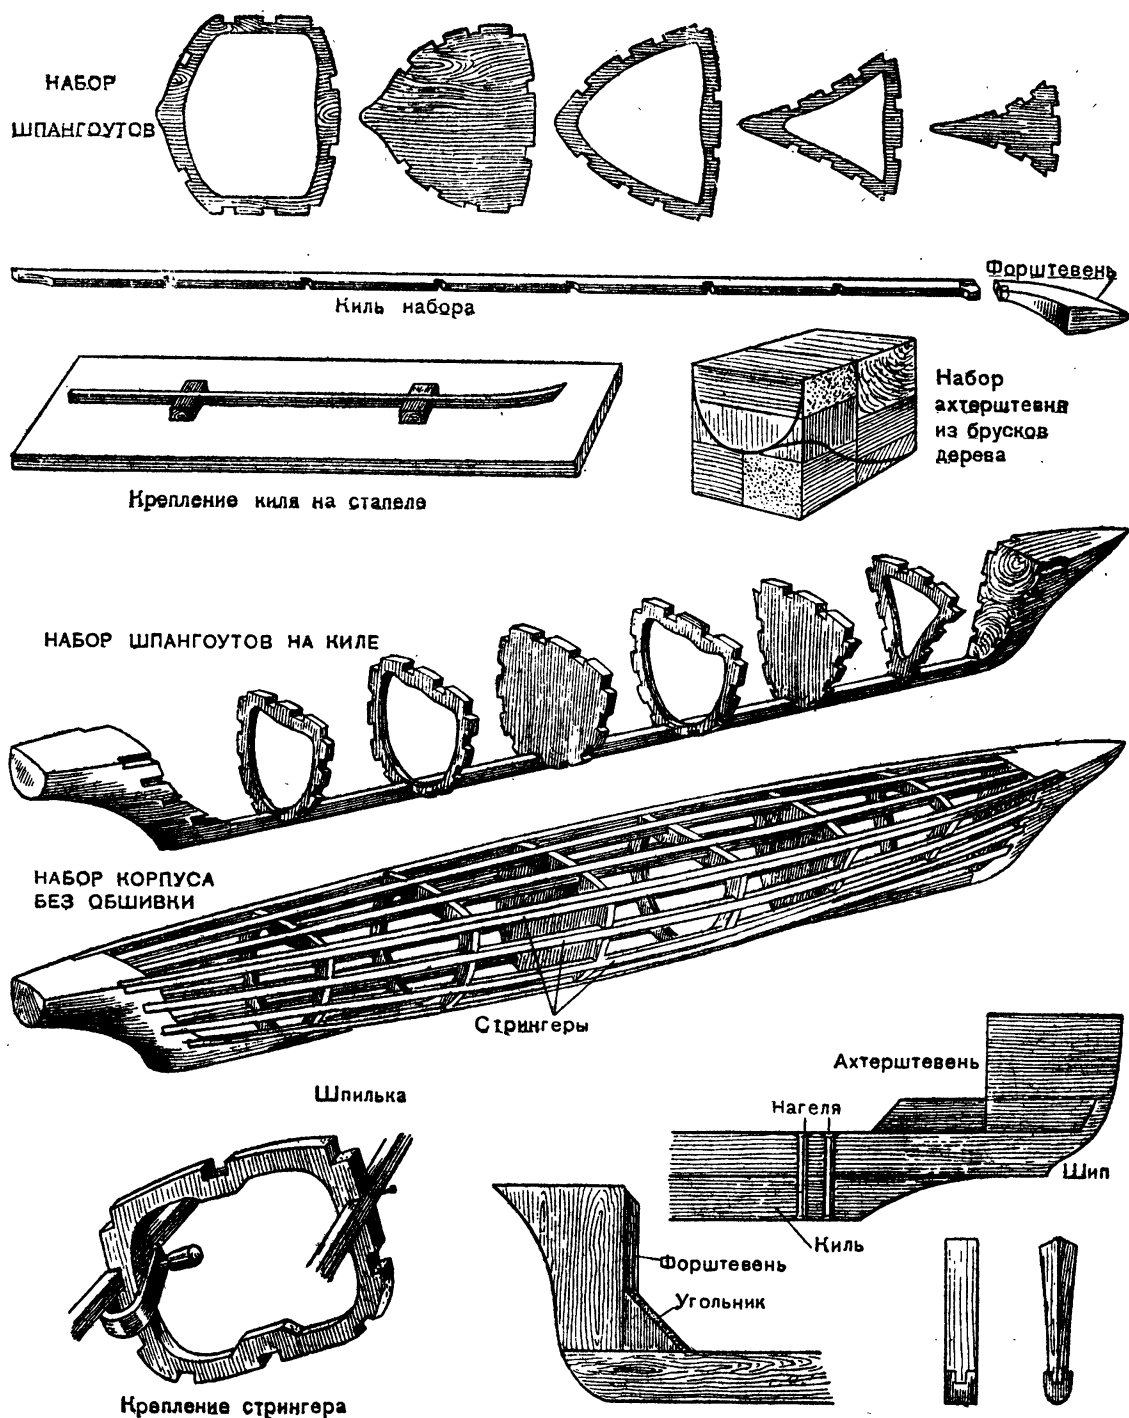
Изготовление корпуса модели корабля наборным способом.
